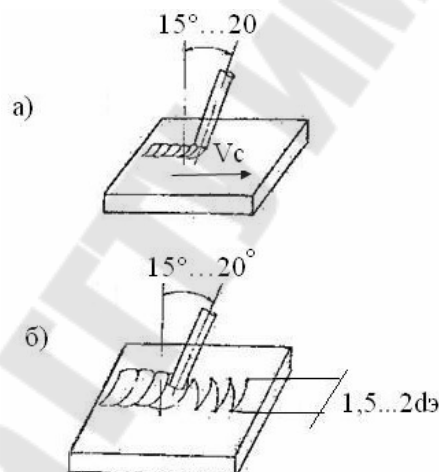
Техника наплавки: а – углом назад; б – с поперечными колебаниями
